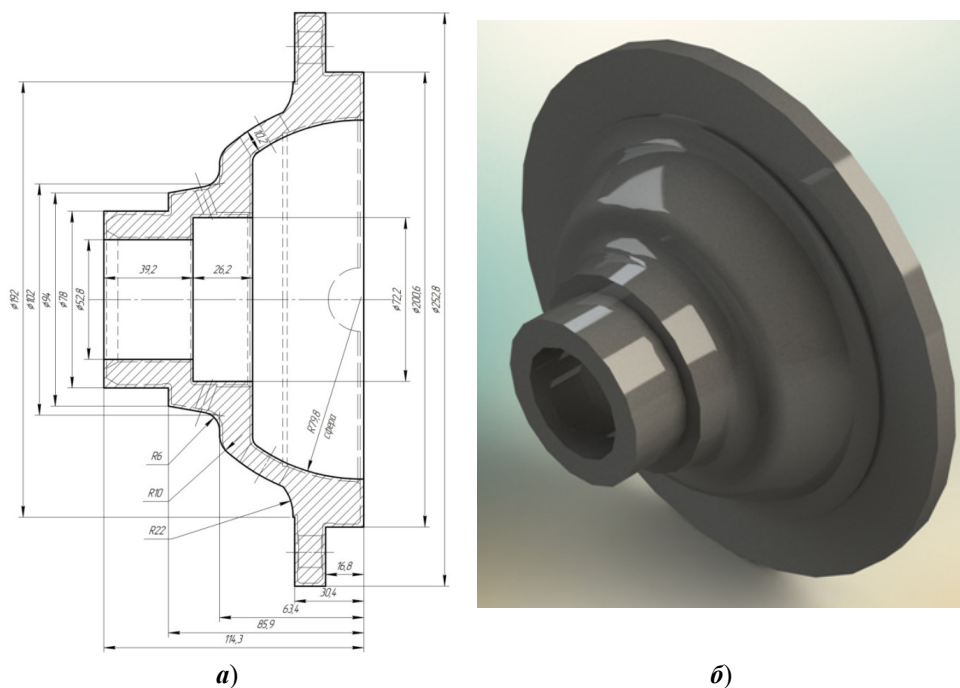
Эскиз заготовки с назначенными размерами (а) и 3D-модель заготовки (б)
